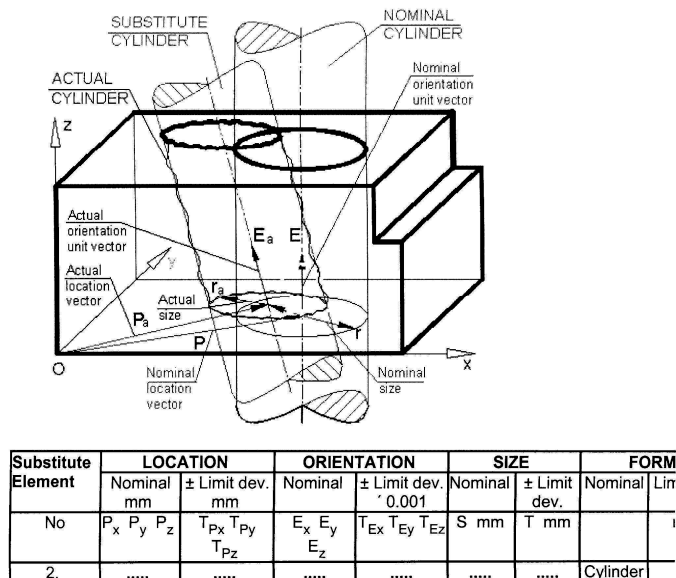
Exemplo de conceito de “*Vectorial Dimensioning and Tolerancing*” (VD&T). Adaptada de [H3]
